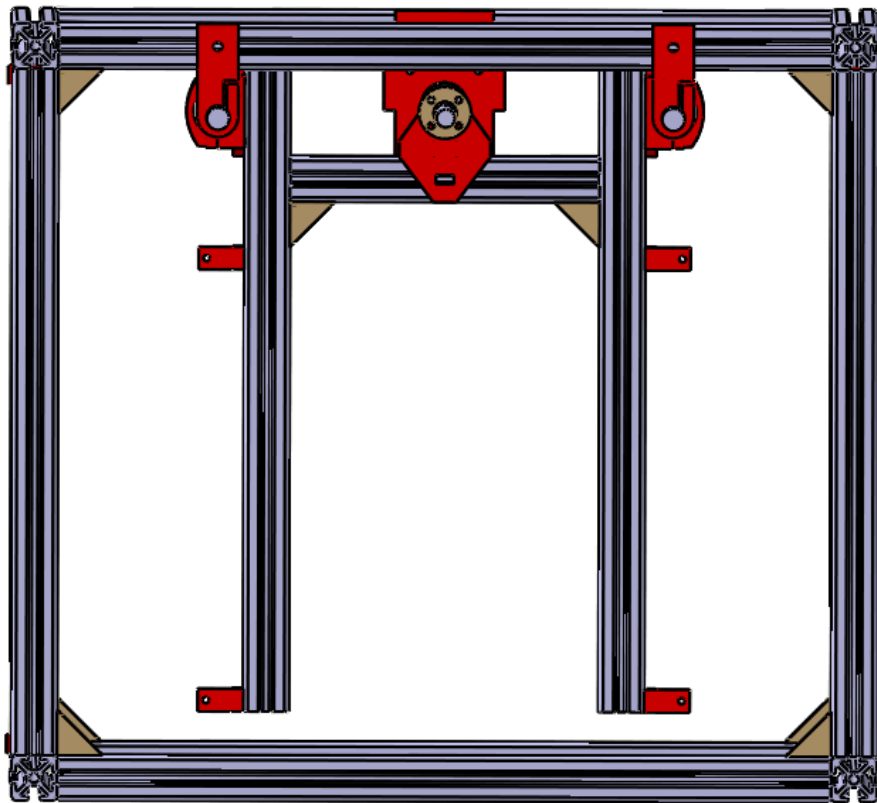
Umístění úchytu motoru a ocelových tyčí osy Z
